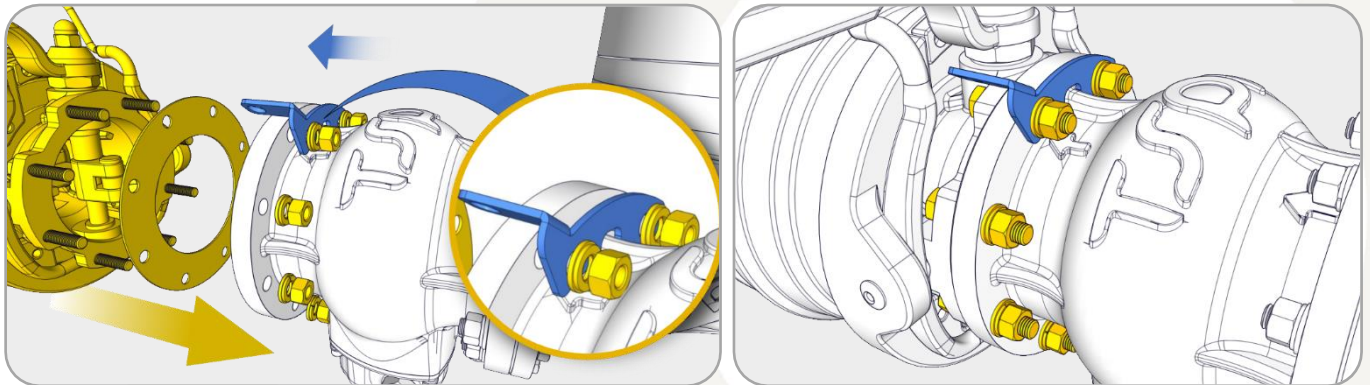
Montagem Acoplador API e do Suporte API Sensor NAMUR
